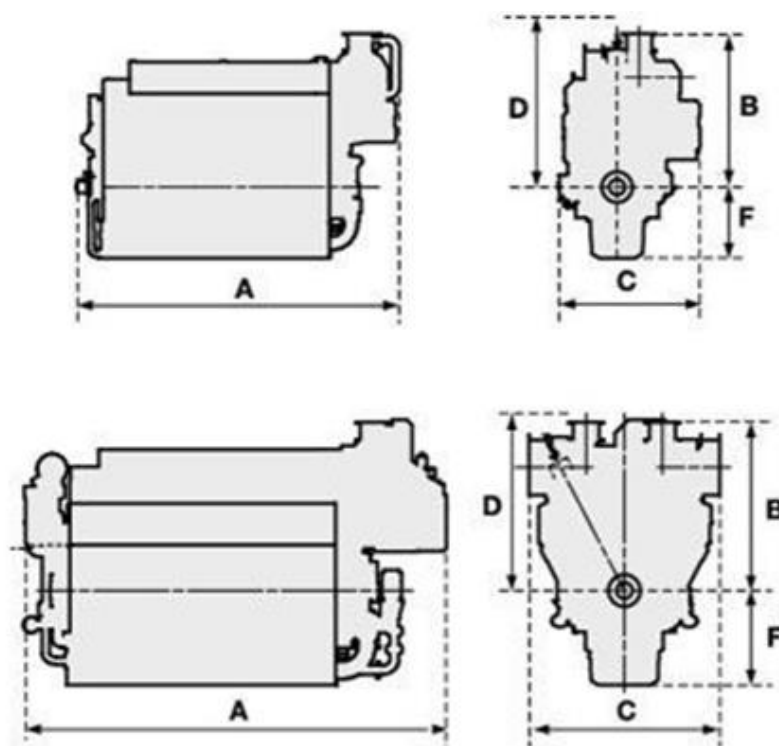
Габаритные присоединительные размеры двигателя «Wartsila 34DF»
